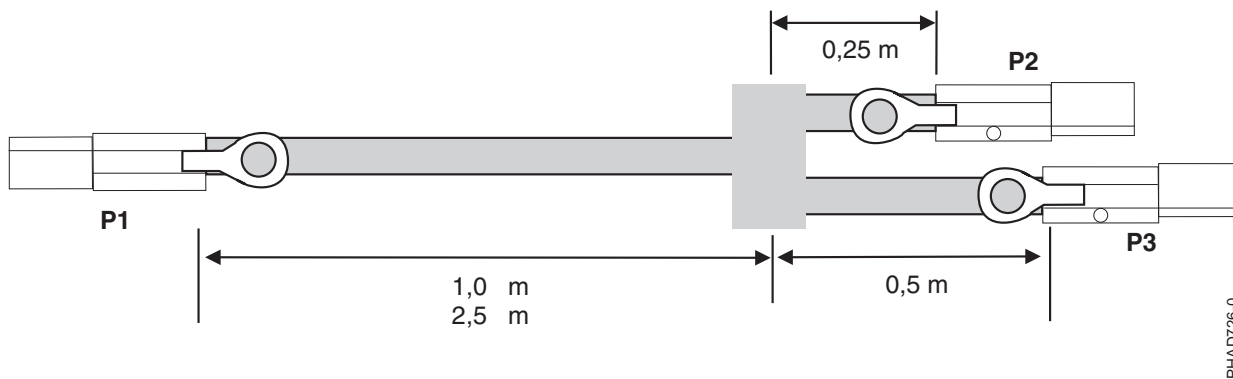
Longitudes de cable de conjunto de cables YI SAS externos
